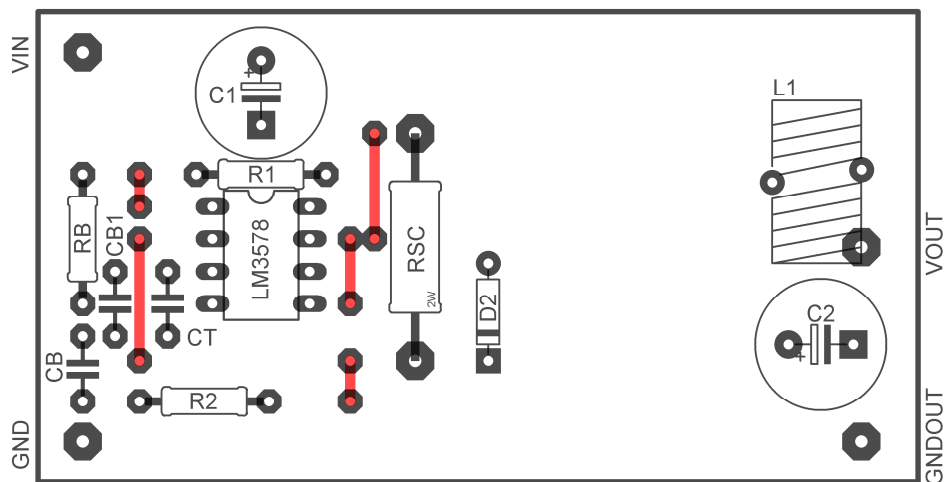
Univerzální schéma zapojení pro všechny tři typy měničů
